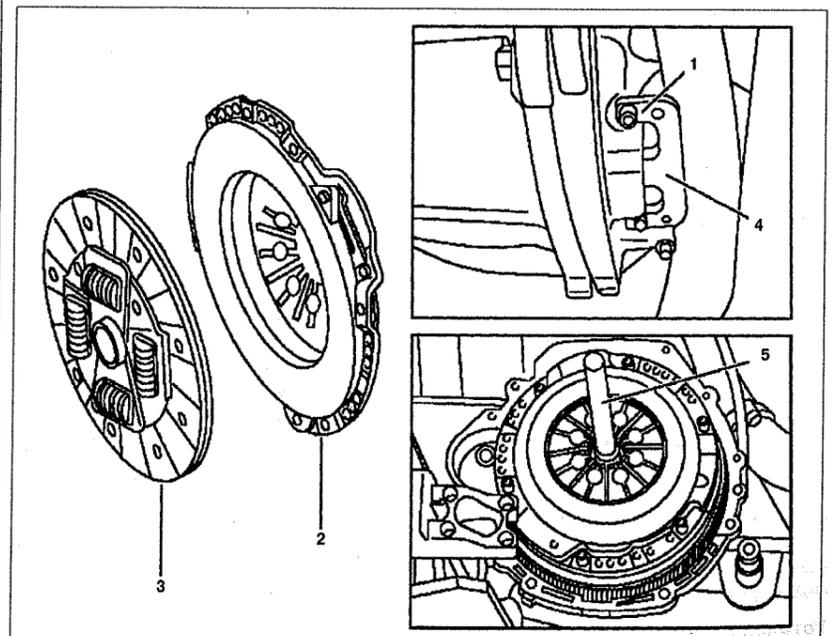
Снятие и установка сцепления на автомобилях с двигателем 611.980:
